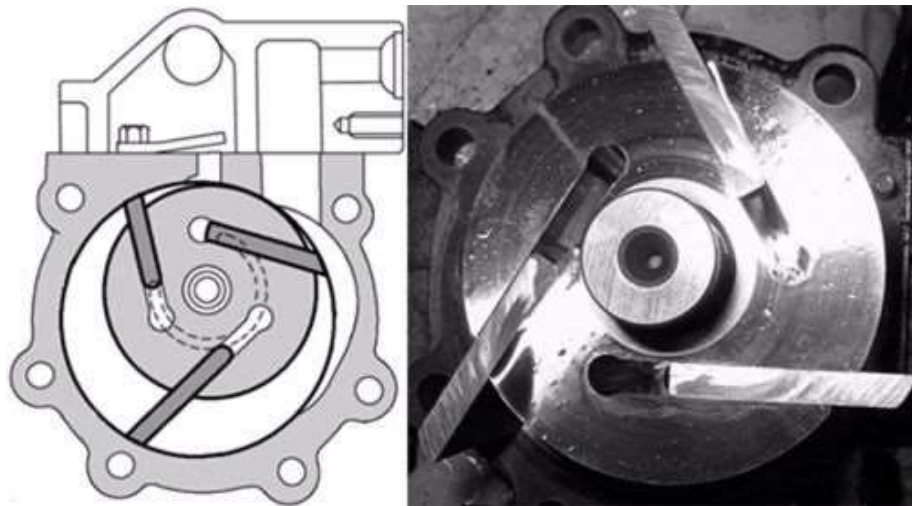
Схема роторно-лопатєвого компресора
